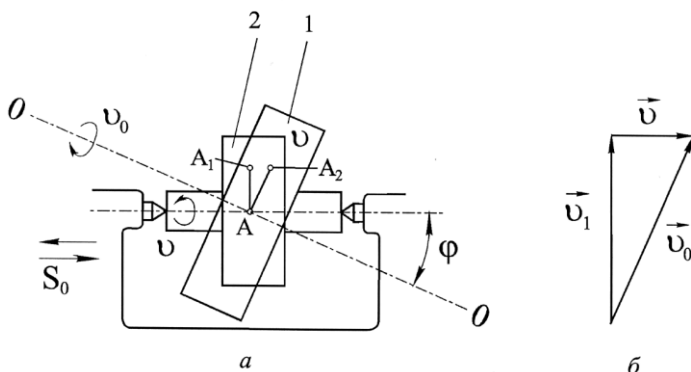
Схема работы дискового шевра (а) и план скоростей при обработке шевром цилиндрических прямозубых колес (б): 1 – шевр; 2 – колесо зубчатое
